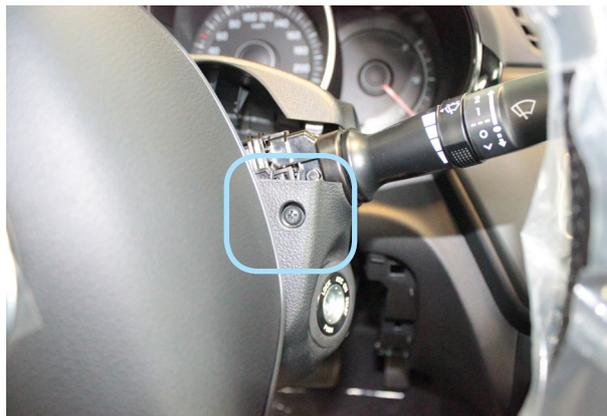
Саморез крепления нижней части кожану рулевого вала справа
